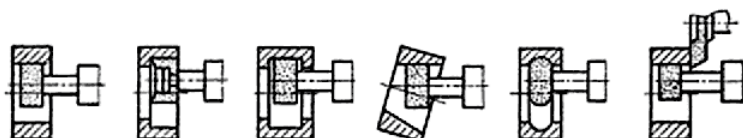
Схемы шлифования на внутришлифовальных станках
